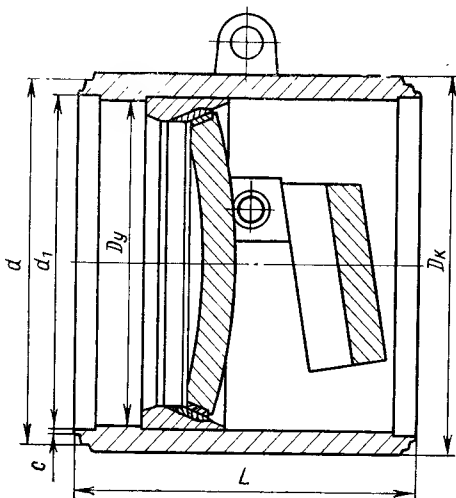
Обратный поворотный клапан Л 44082 на $p_y=16$ МПа.
